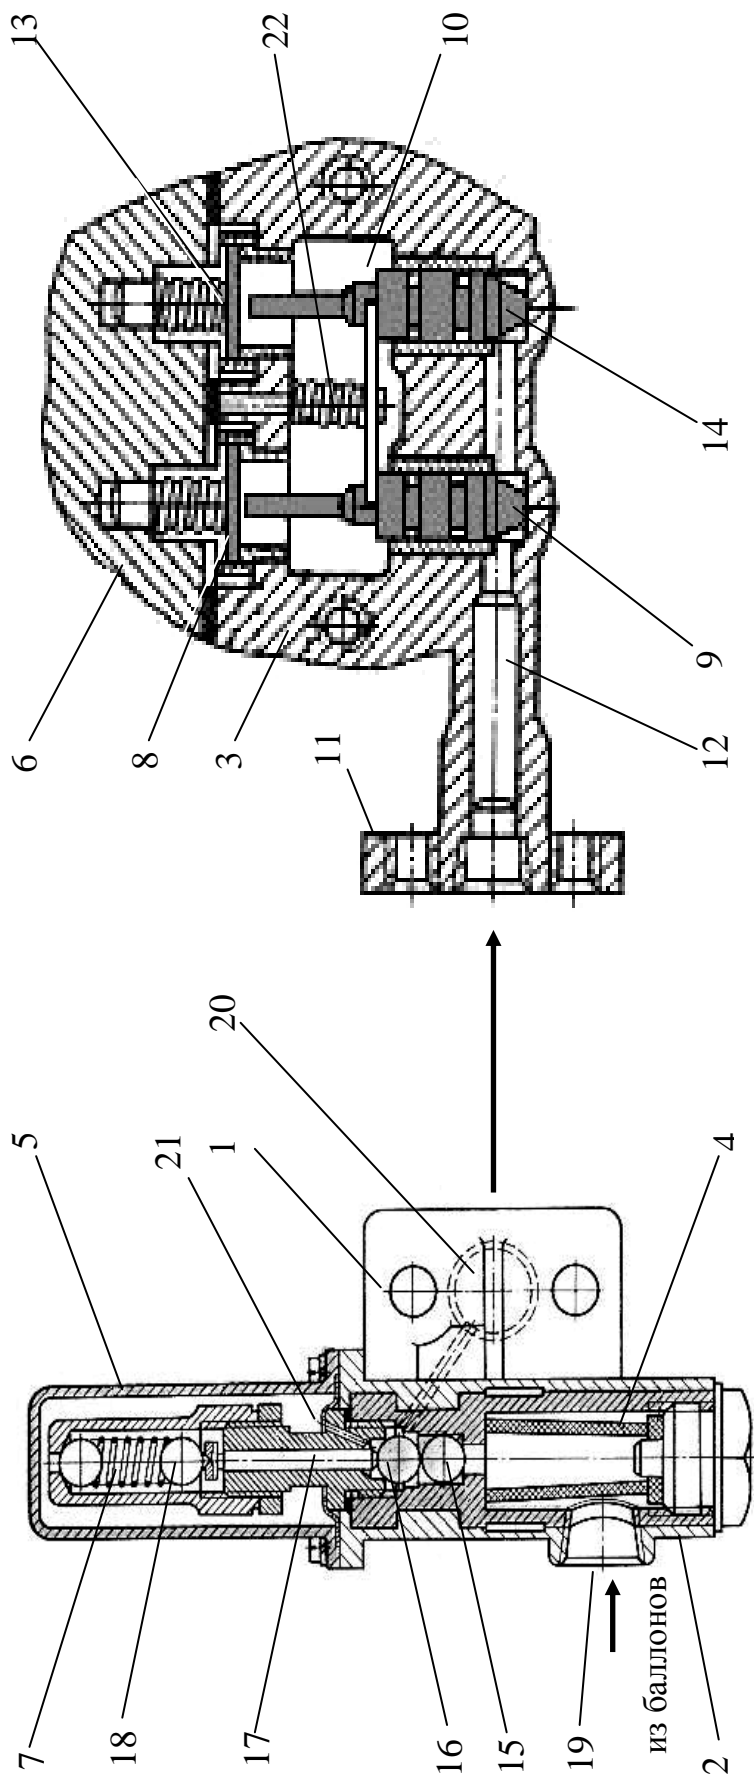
Система регулирования давления сжатого воздуха, подаваемого в баллоны тормозного привода : 1 – фланец регулятора давления для его крепления на блоке цилиндров компрессора; 2 – корпус регулятора давления; 3 – блок цилиндров компрессора; 4 – фильтр регулятора давления; 5 – кожух регулятора давления; 6 – головка блока цилиндров компрессора; 7 – пружина регулятора давления; 8 – впускной клапан 1-го цилиндра компрессора; 9 – плунжер впускного клапана 1-го цилиндра компрессора; 10 – впускной канал компрессора; 11 – фланец на блоке цилиндров компрессора для крепления регулятора давления; 12 – канал от регулятора давления; 13 – впускной клапан 2-го цилиндра компрессора; 14 – плунжер впускного клапана 2-го цилиндра компрессора; 15 – впускной канал компрессора; 16 – выпускной клапан регулятора; 17 – выпускной клапан регулятора; 18 – шток клапанов регулятора; 19 – упорный шарик; 20 – впускное отверстие регулятора; 21 – атмосферное отверстие регулятора; 22 – пружина
